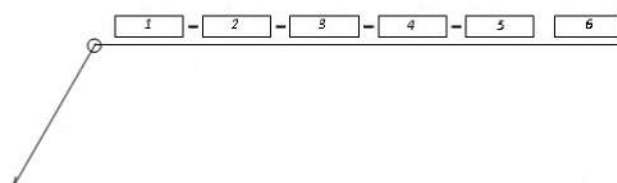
Обозначение на чертеже сварного шва (в общем виде)
